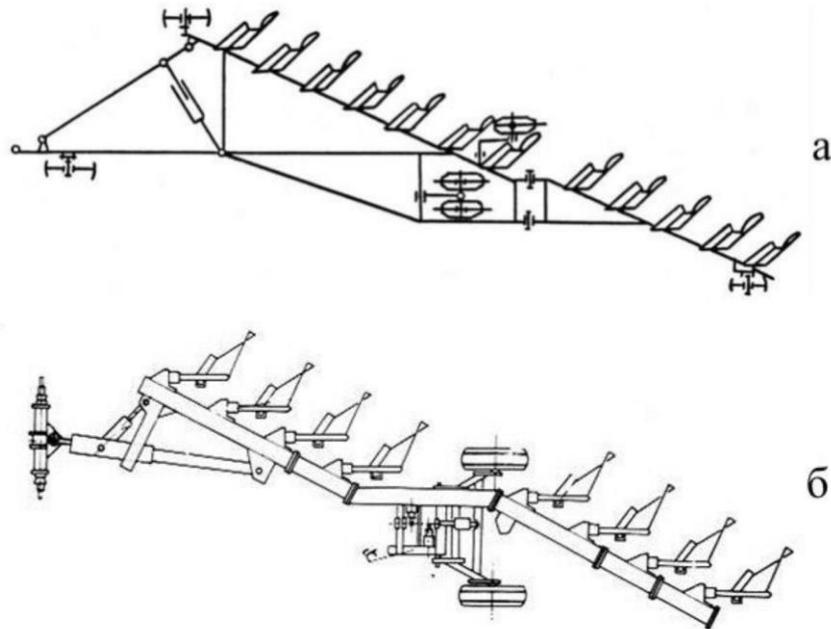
Схеми багатокорпусних напівнавісних плугів з шарнірною рамою: а – 12-корпусний плуг ПШ-12-40М; б – 8-корпусний плуг фірми «KuhnHardt».
